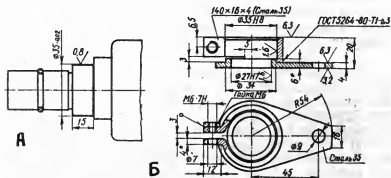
а — доработка корпуса прерывателя; б — скоба.
